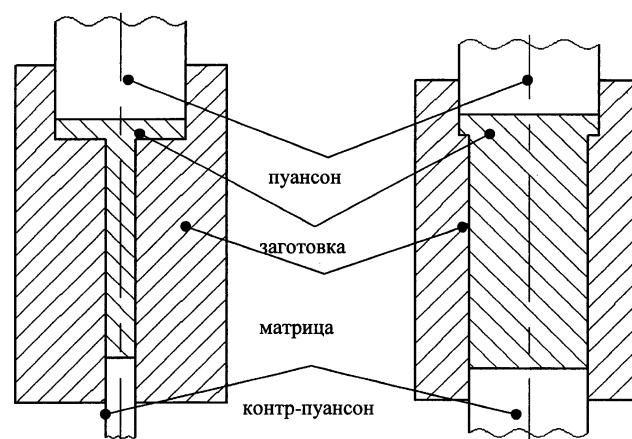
Схема инструмента для объемной штамповки: а — боковой разрез; б — фронтальный разрез
